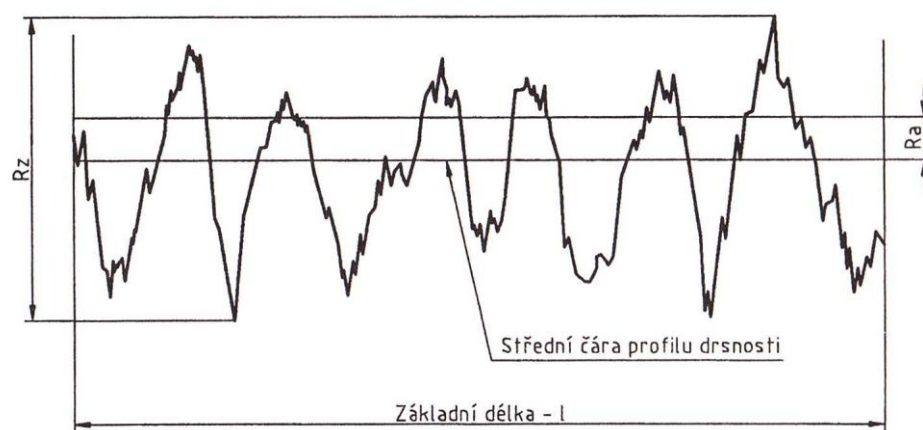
Průmět profilu povrchu do roviny [10]
